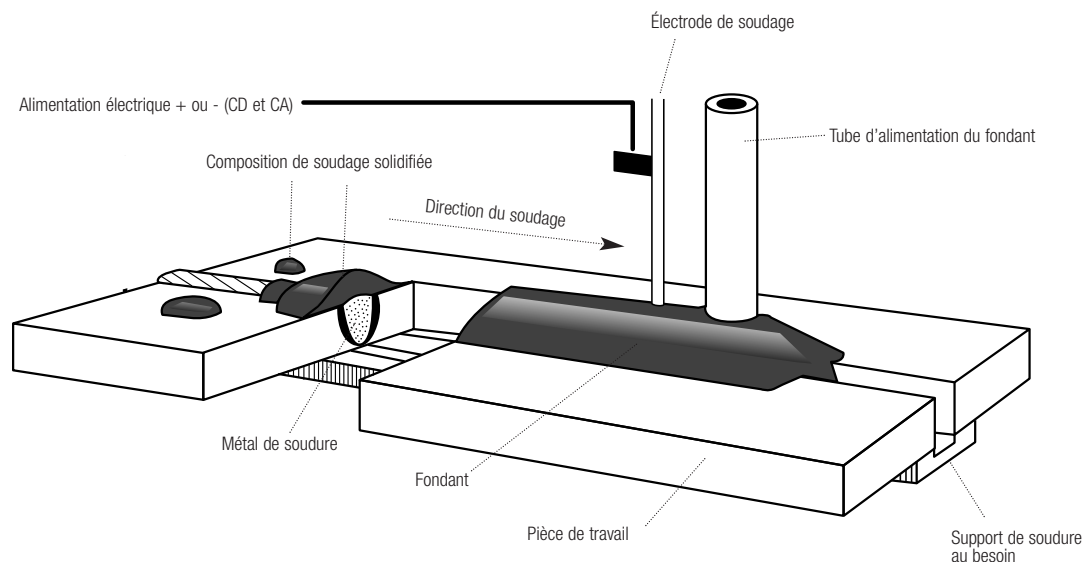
Arrangement de soudage à l'arc submergé (SAW)
